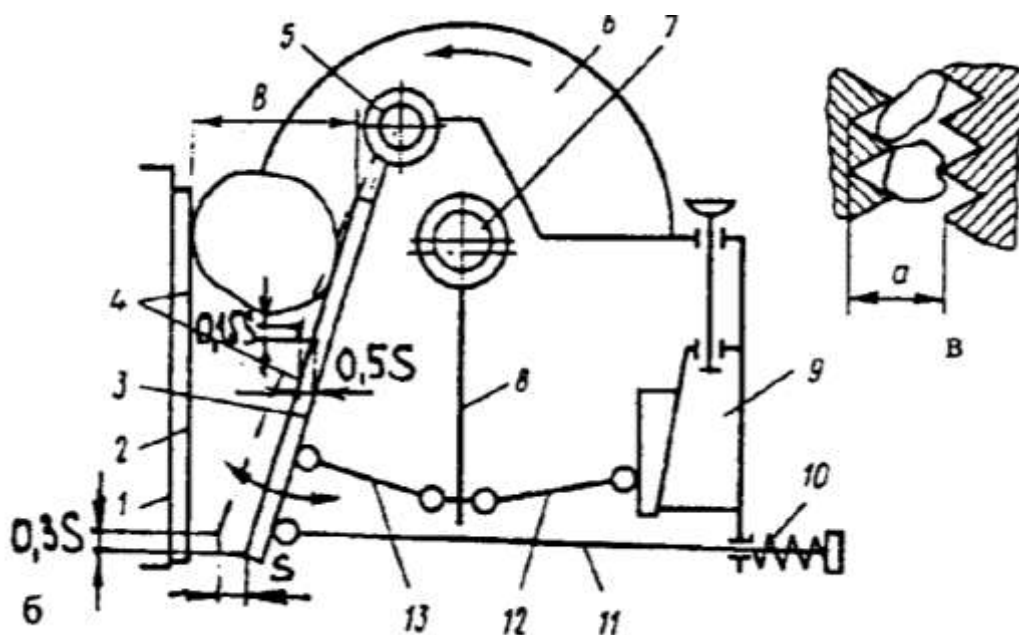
Щокова дробарка із простим рухом щоки
